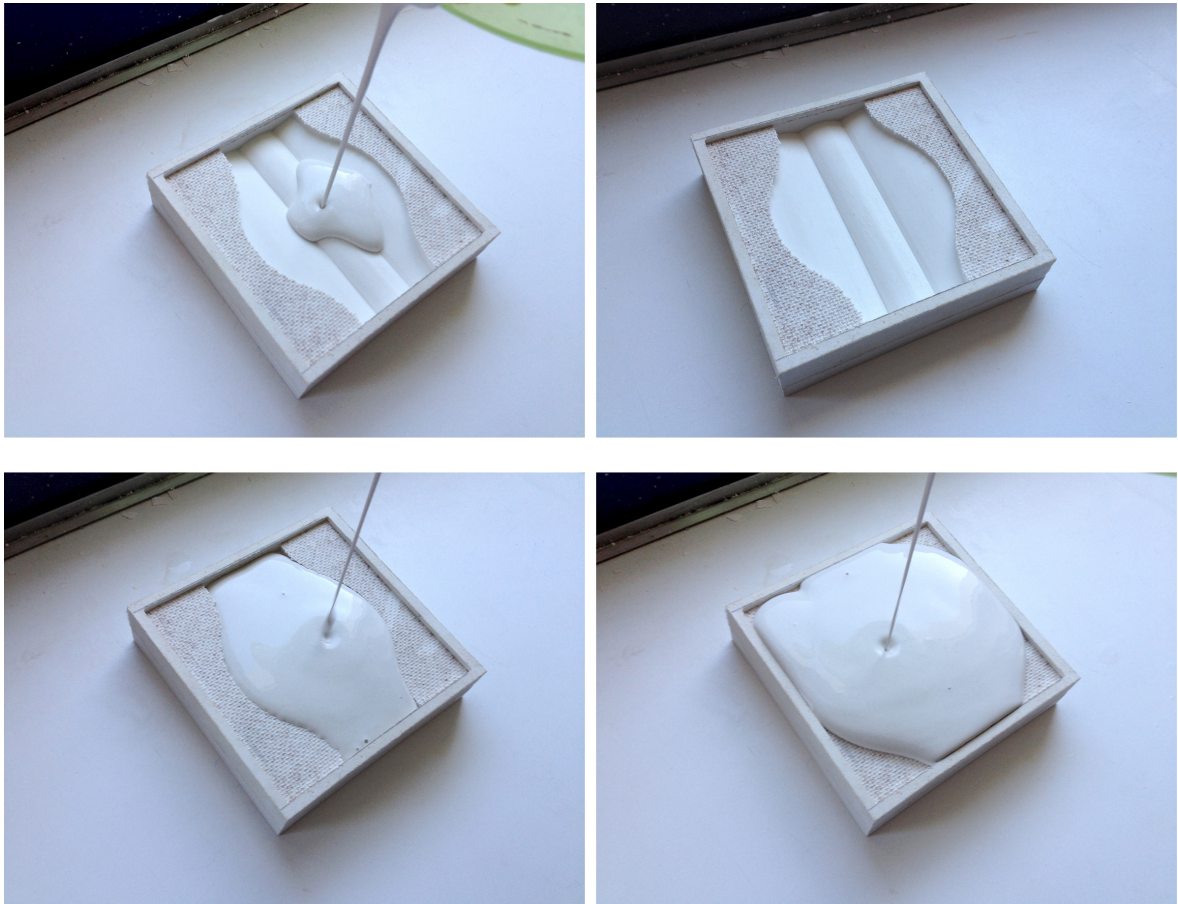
Vazamento do gesso para o molde em borracha de silicone.
